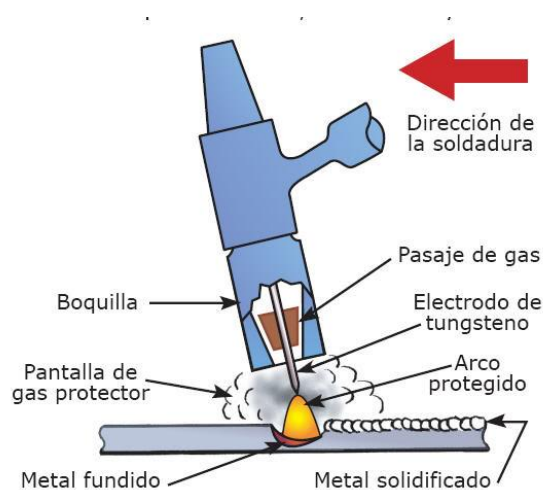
Soldadura TIG (Tagmagroup.com.ar, 2016)
